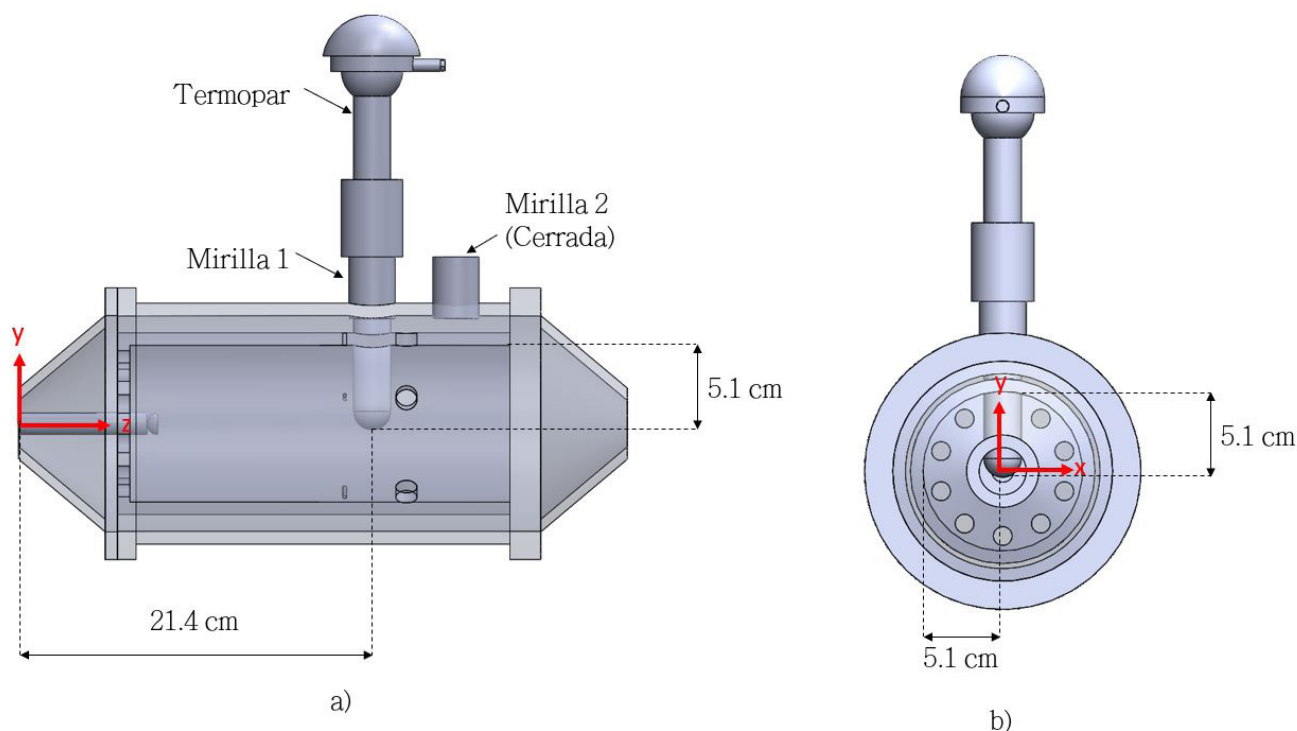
Vistas del prototipo de cámara de combustión, utilizando SolidWorks: a) Vista longitudinal, plano (y, z); b) Vista transversal, plano (x, y).
